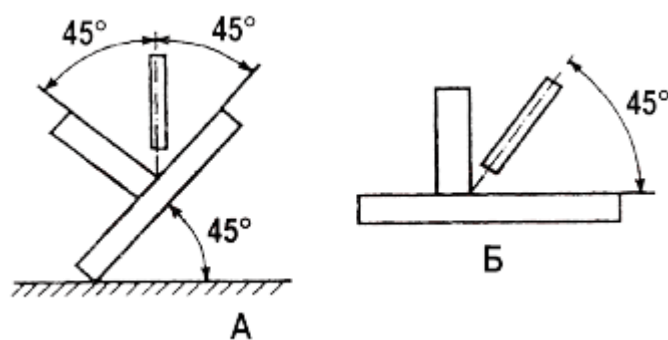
Техника выполнения угловых швов. Способы удержания сварочной ванны ручной дуговой сварке: А – «в лодочку»; Б – наклонным электродом.
